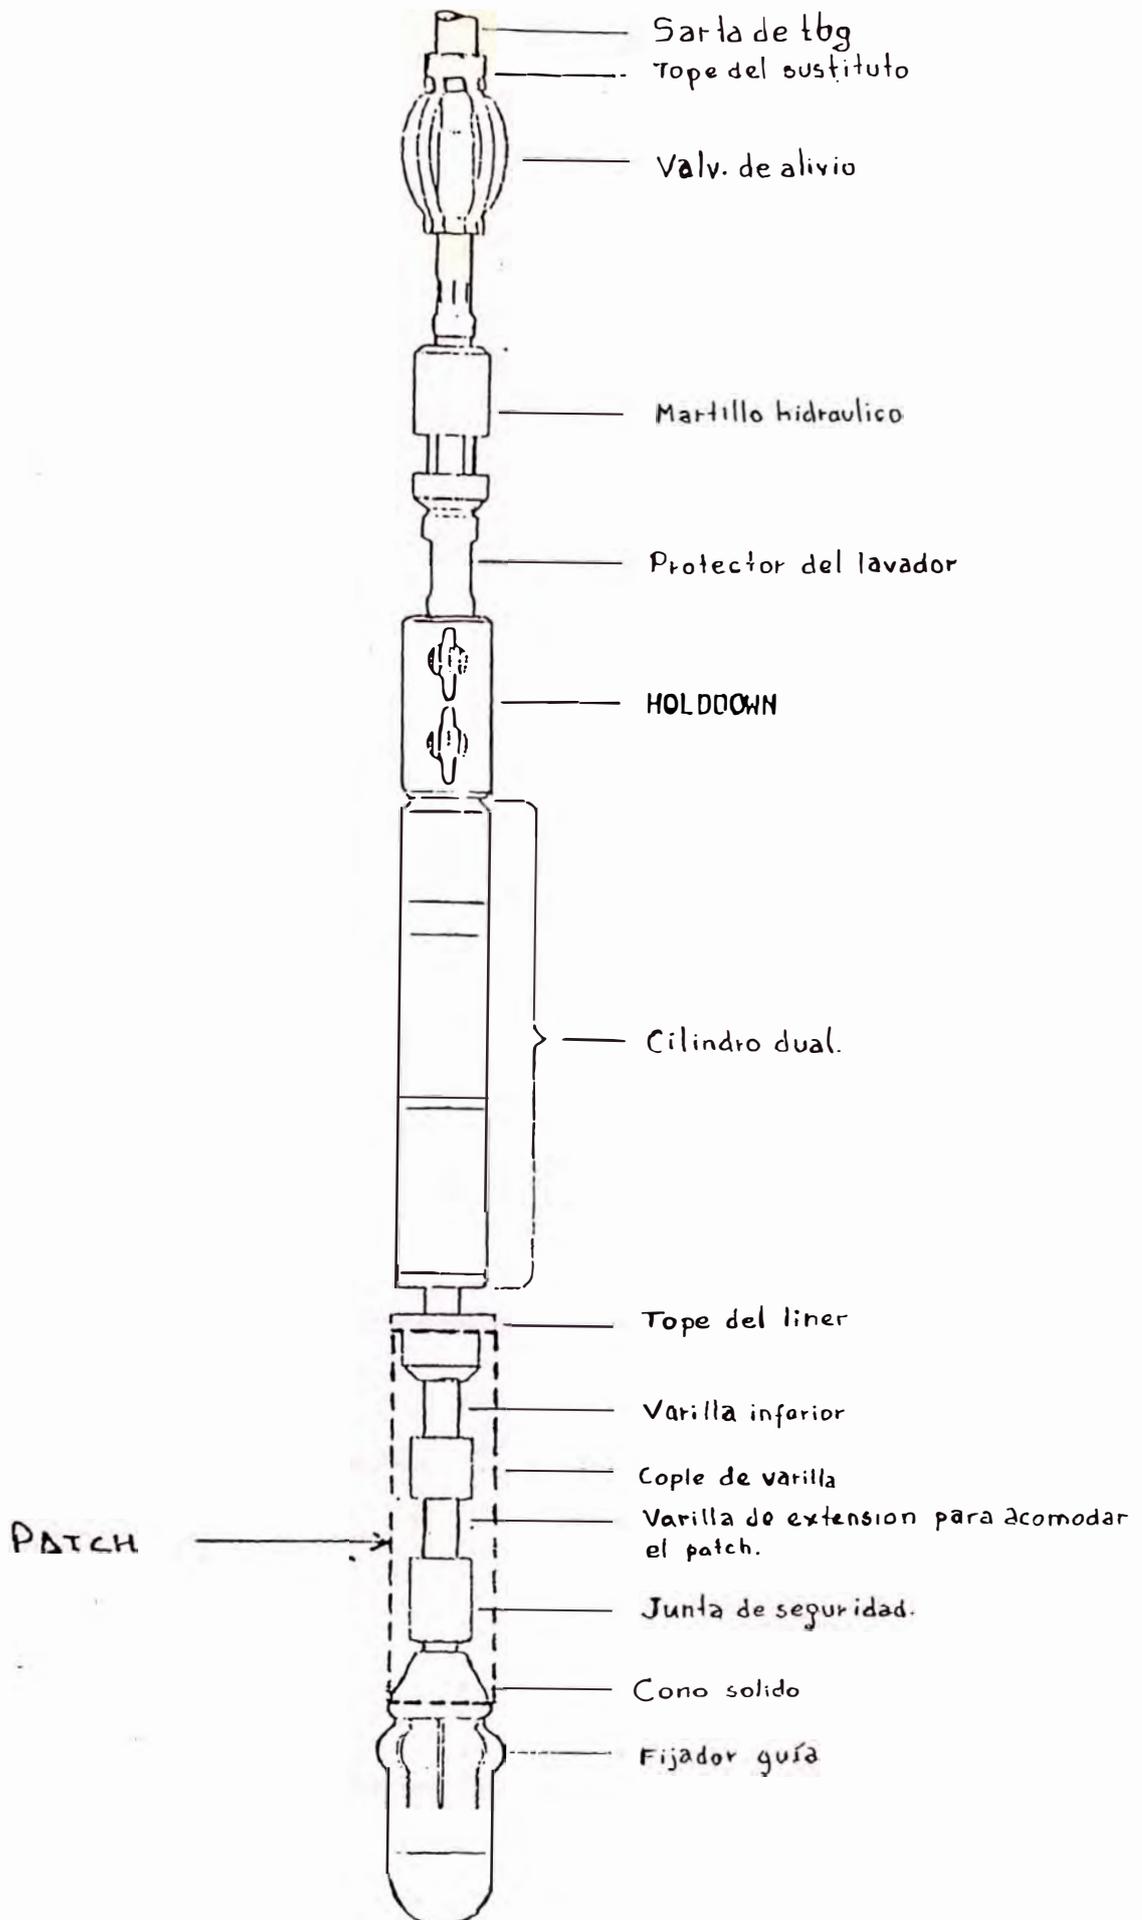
A Componentes del Howco Steel Liner Casing Patch
